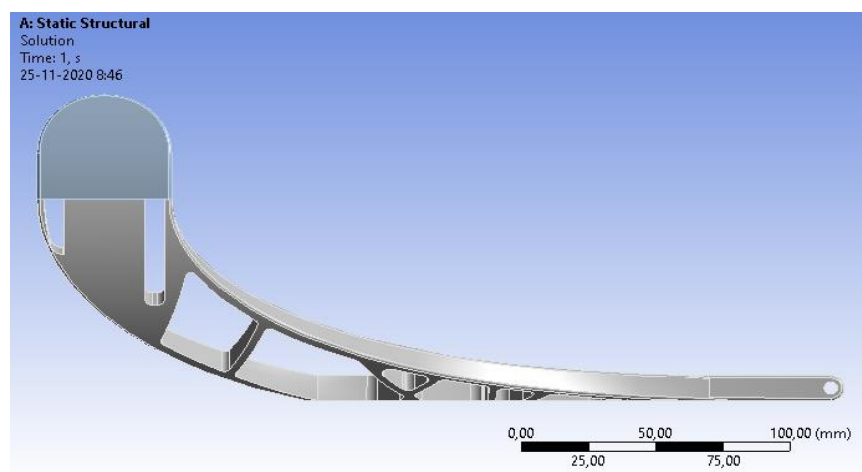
Vista 4 rediseño N°1 de eslabón pierna izquierda.
